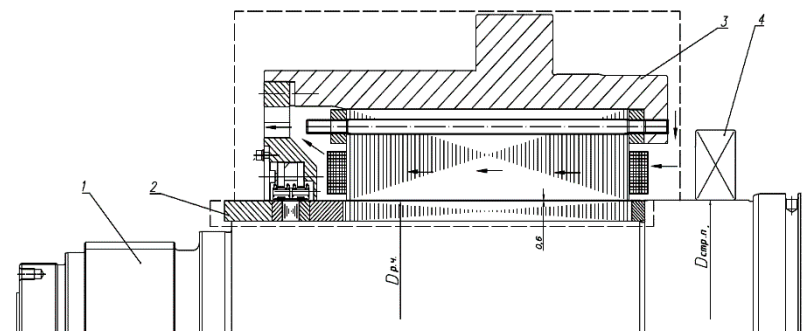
Схема измененной конструкции сборного радиального магнитного подшипника производства
